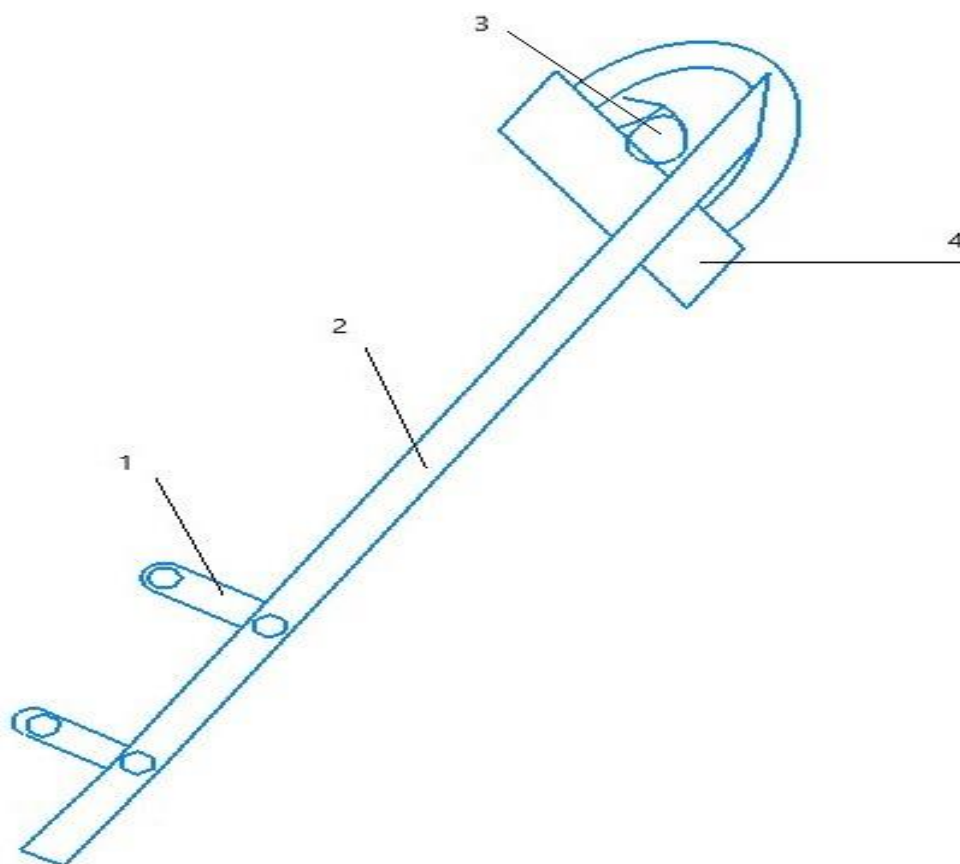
Приспособления для измерения угла поворота рычага подвески: 1 – уголок монтажный, 2 – линейка измерительная, 3 – болт осевой, 4 – транспортир.
